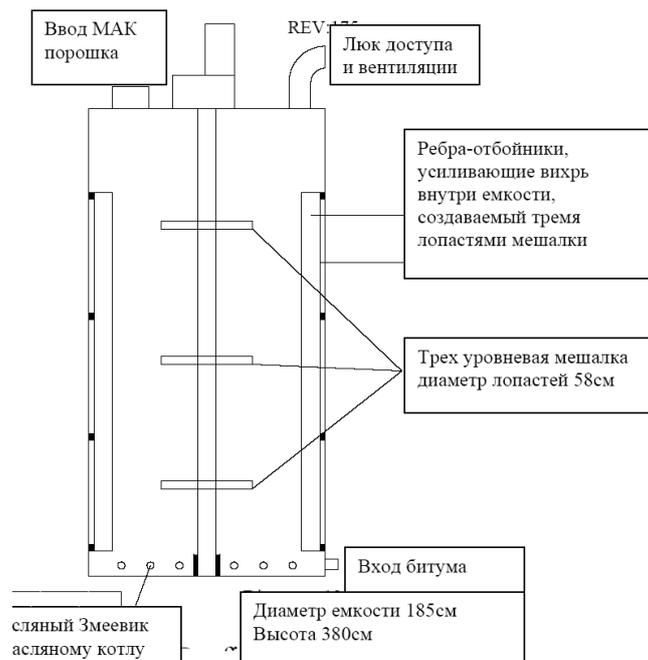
Схема смесителя для приготовления вяжущего Мультигрейд
